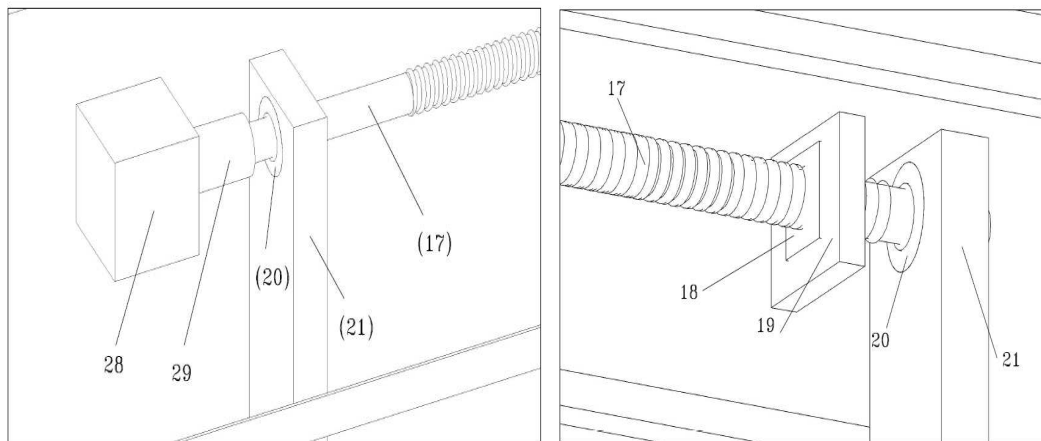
Esquema de Transmisión Motor – Tornillo-Tuerca.
